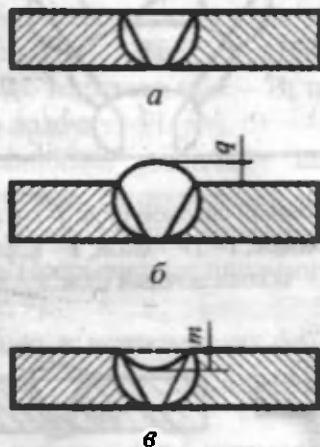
Сварные швы: а – нормальные; б – выпуклые; в – вогнутые
